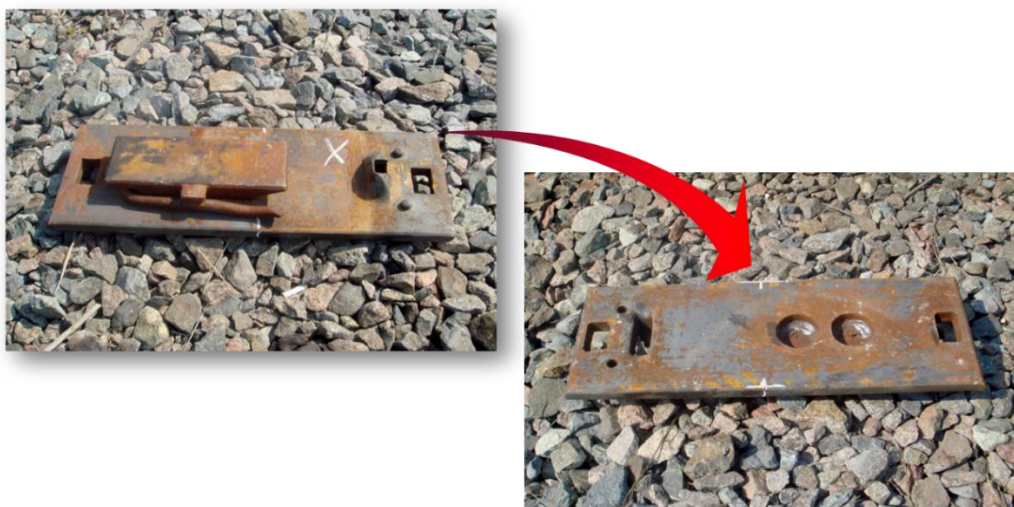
Подкладка с подушкой, изготовленная с использованием технологии сварки
